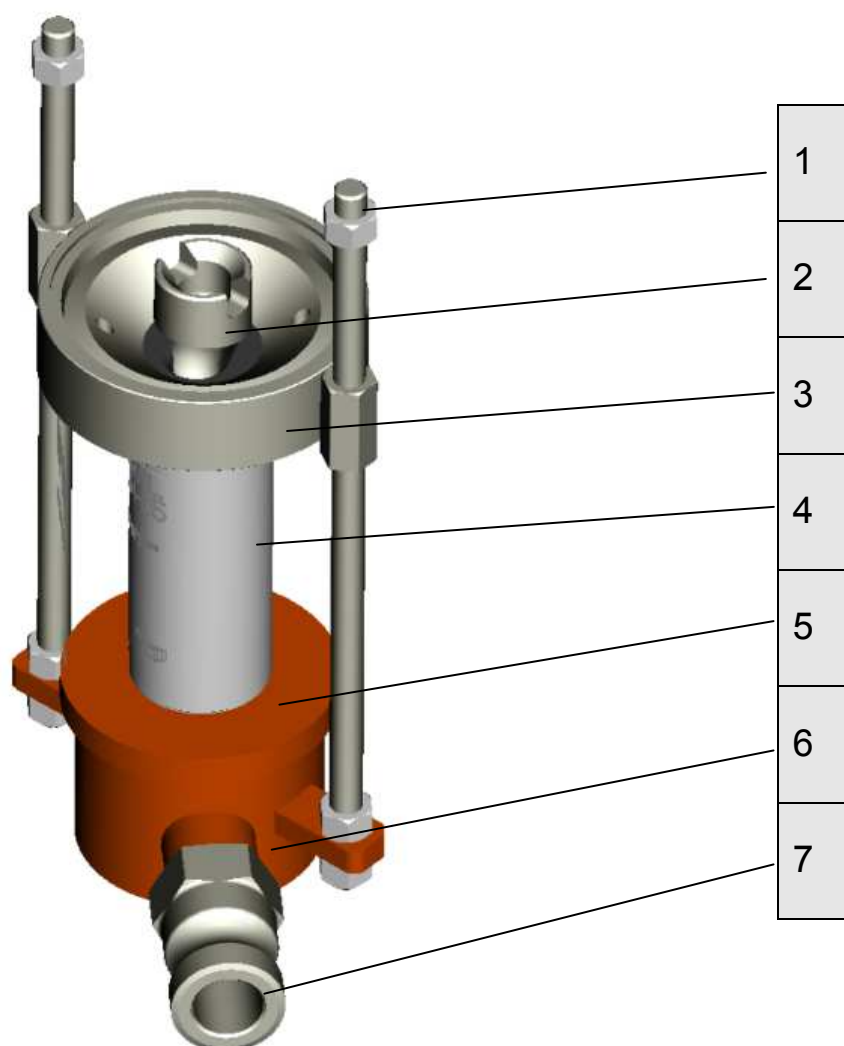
Vue d'ensemble Rotomix pour pompe B 00 14 73 53
